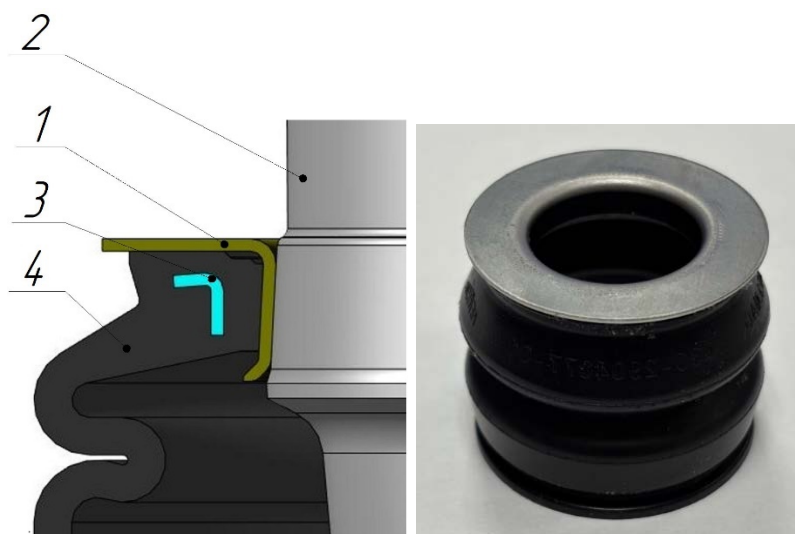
Внешний вид уплотнительной системы шарового шарнира с отсекателем из нержавеющей стали: 1 – отсекатель; 2 – палец шаровой (с покрытием ZnNi); 3 – интегрированное кольцо; 4 – чехол защитный
